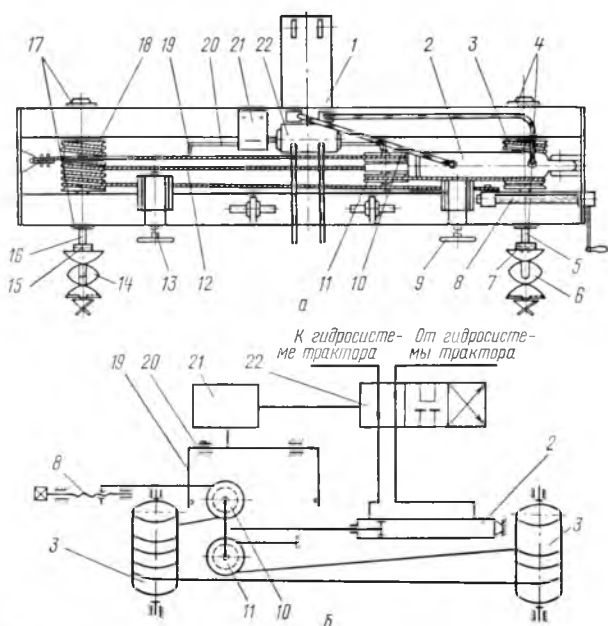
Схемы ямокопателя ЯС-2 (а, вид спереди) и гидромеханического привода рабочих органов (б)
